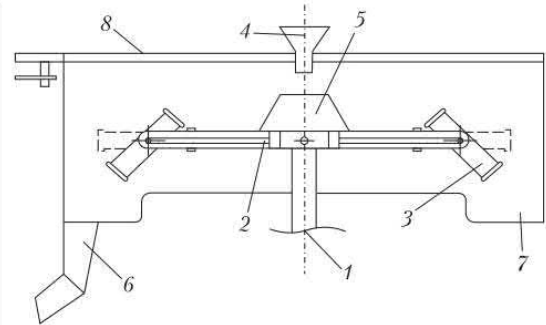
Стаканчиковая центрифуга: 1 – вал ротора; 2 – крестовина; 3 – фильтрующие стаканы; 4 – верхняя воронка; 5 – питающий патрубок; 6 – сливной патрубок; 7 – корпус центрифуги; 8 – крышка центрифуги
